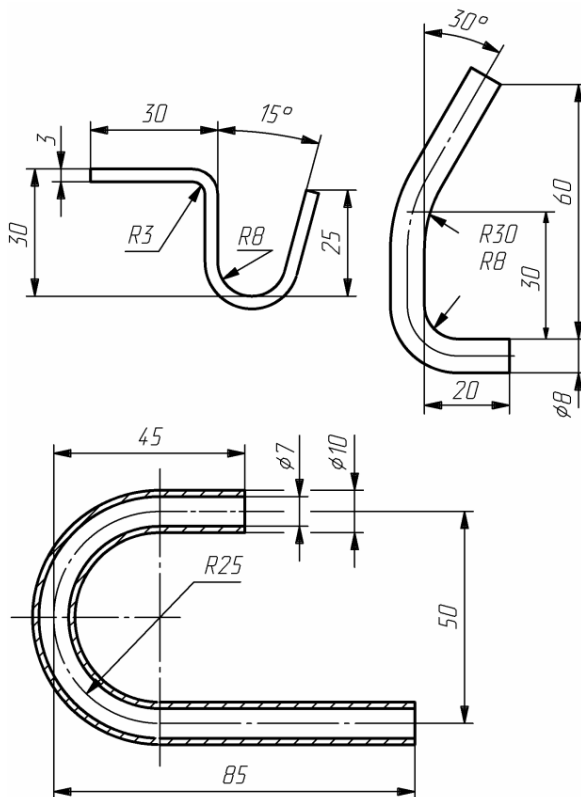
Кресленик деталей, виготовлених гнуттям.
